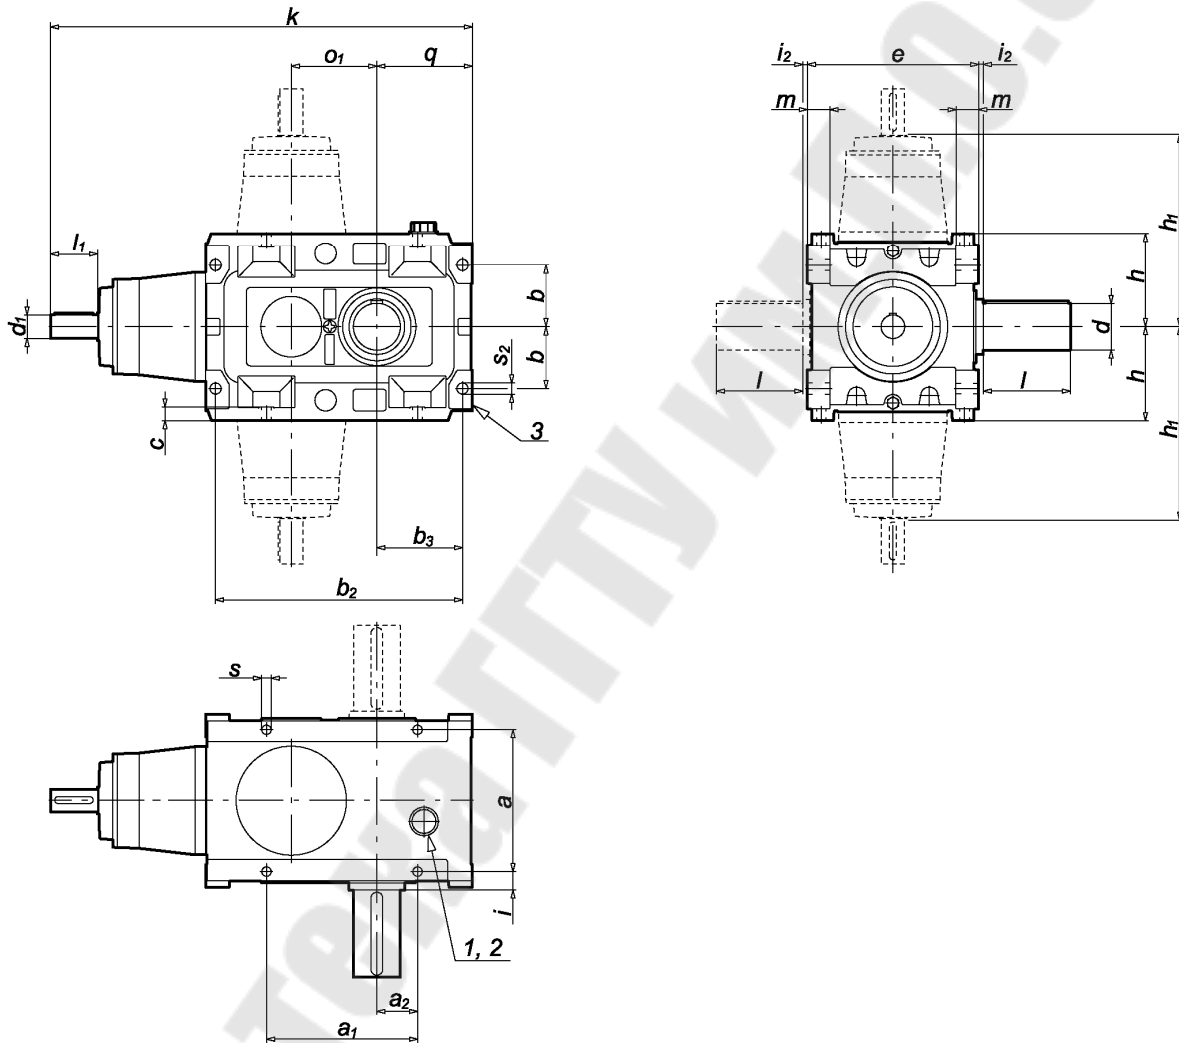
Редукторы двухступенчатые 5КЦ1 – 180...280ES, на лапах:
